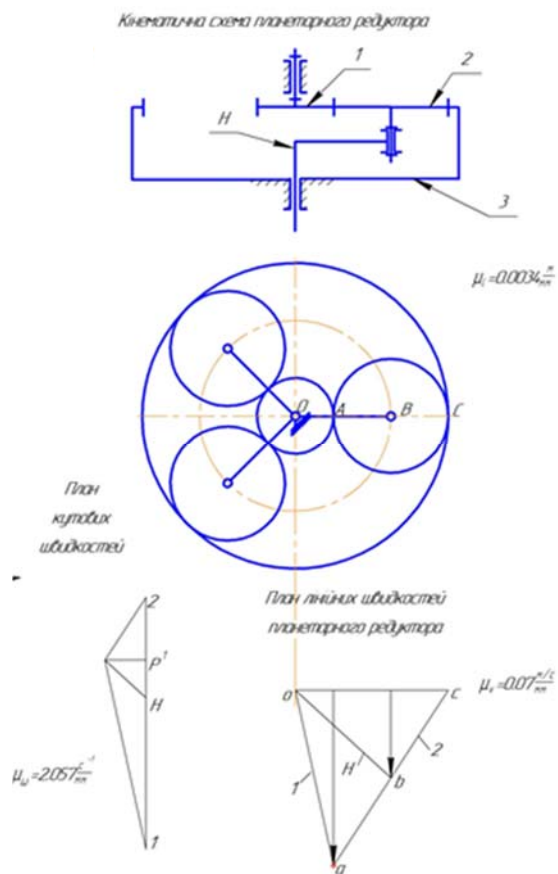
Синтез кінематичної схеми планетарного редуктора
